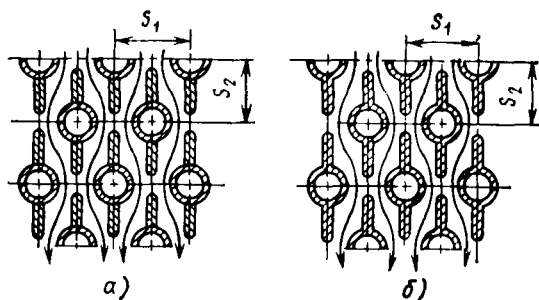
Плавниковые и с приварными ребрами трубы:
